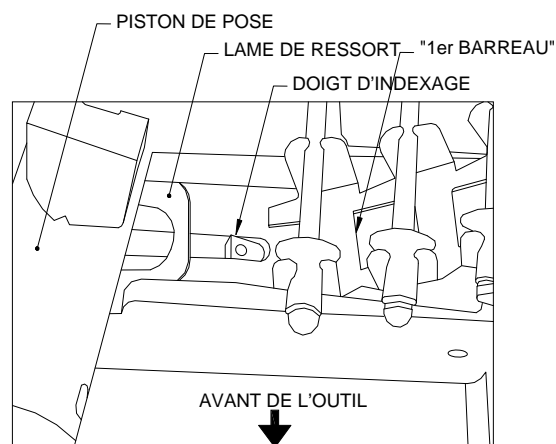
CHARGEMENT DU RUBAN DE RIVETS
